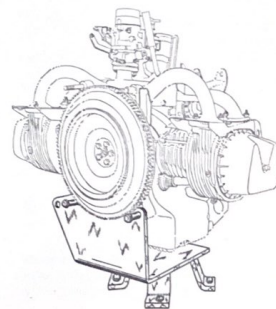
Utilización del soporte MR-3053-50 con el motor en posición horizontal.
